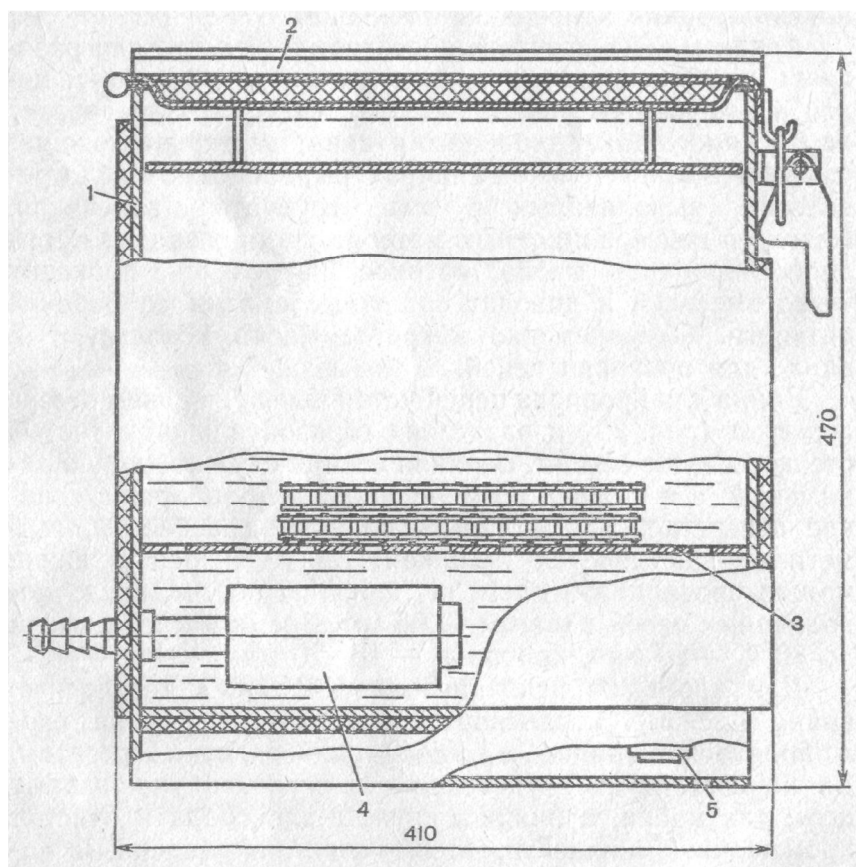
Ванна для проварки втулочно-роликовых цепей:
